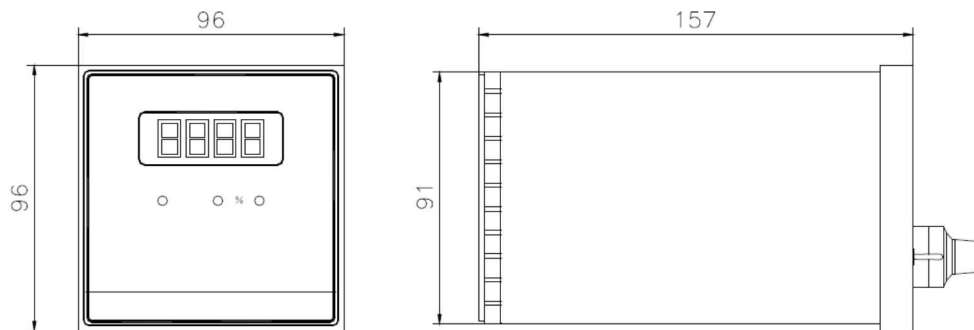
Габаритные размеры корпуса контроллеров D08-1K
